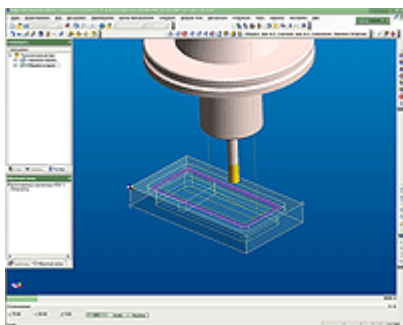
Edgescam. Обработка первой стороны детали (траектория движения фрезы).
